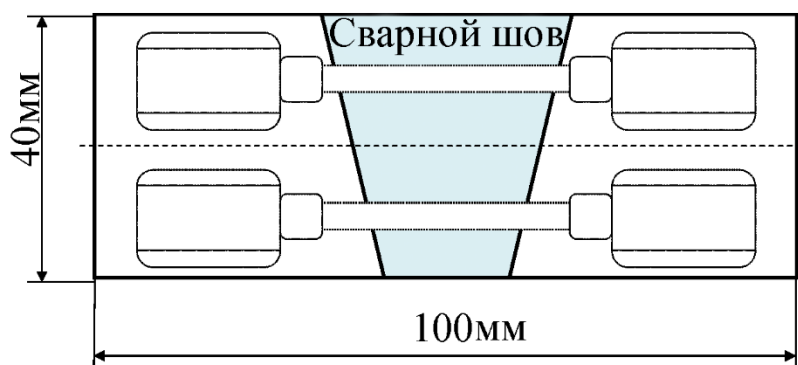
Схема вырезки образцов из сварного соединения для испытаний на длительную прочность.
